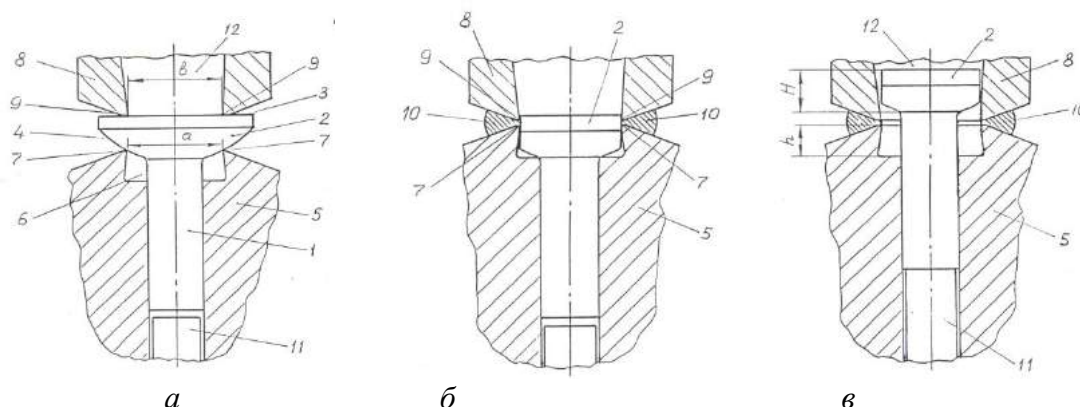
Положение инструмента и заготовки на отдельных этапах процесса обрезки граней: а - начальный момент процесса врезания головки в матрицу; б – положение заготовки и инструмента в конечный момент врезания пуансона и матрицы в головку; в – дорезание головки с отделением срезаемого металла и проталкиванием изделия через отверстие пуансона.
